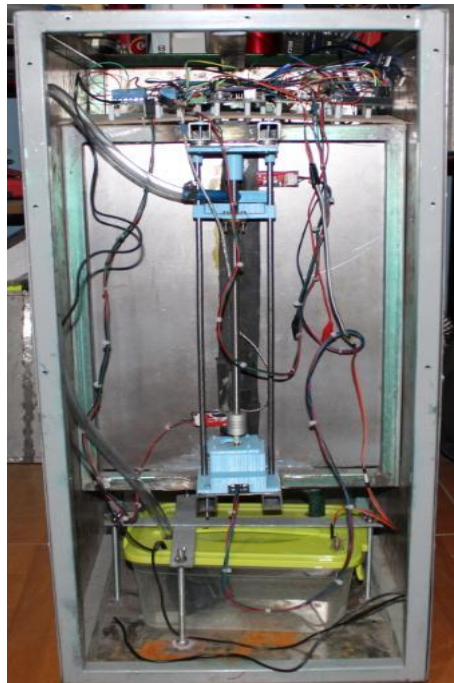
Montaje del sistema de refrigerante y soporte de motor.
